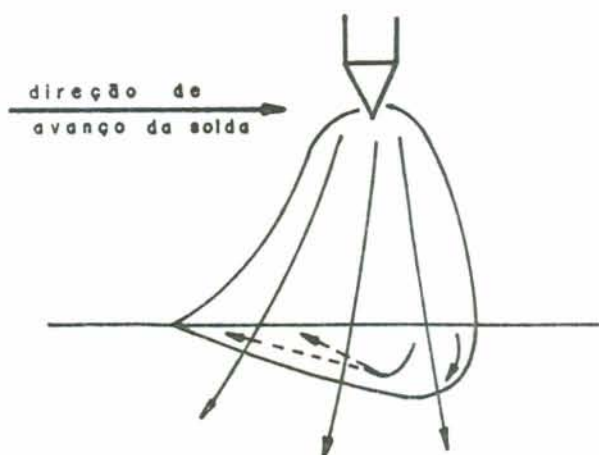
Aspecto do movimento do metal fundido conforme o avanço do arco [22].
